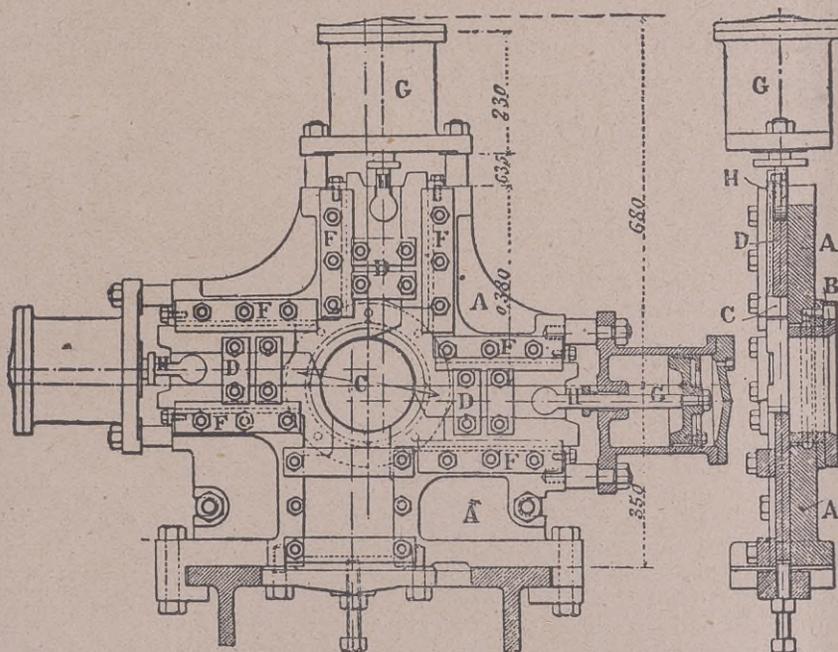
und 3 — Ansicht und Querschnitt der Abstechmaschine mit drei Abstechköpfen
